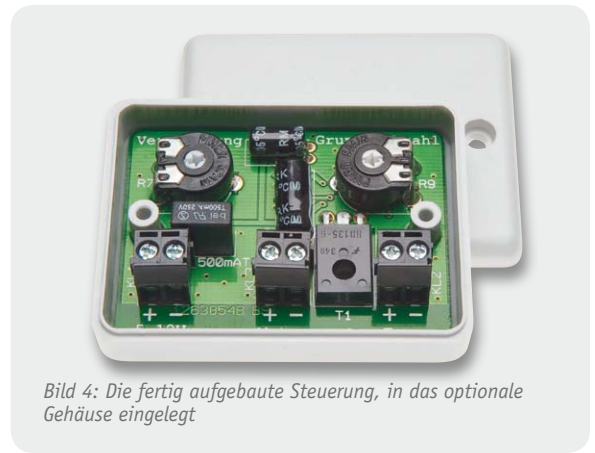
Die fertig aufgebaute Steuerung, in das optionale Gehäuse eingelegt
